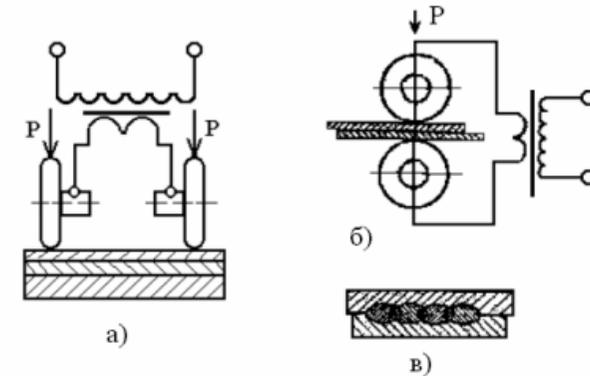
Схема роликовой контактной сварки: а – односторонняя; б – двухсторонняя; в – разрез сварного шва
